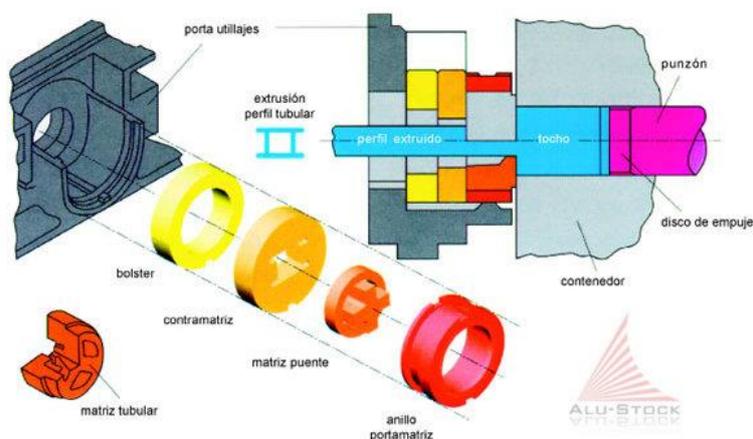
Extrusión y matriz de un perfil hueco (alu-stock.com).
